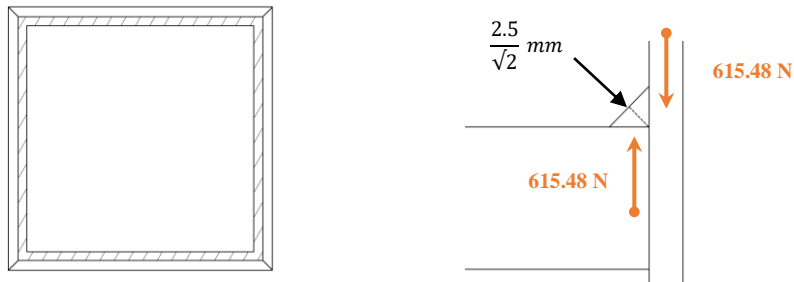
Vista superior de estructura soporte y junta de soldadura
